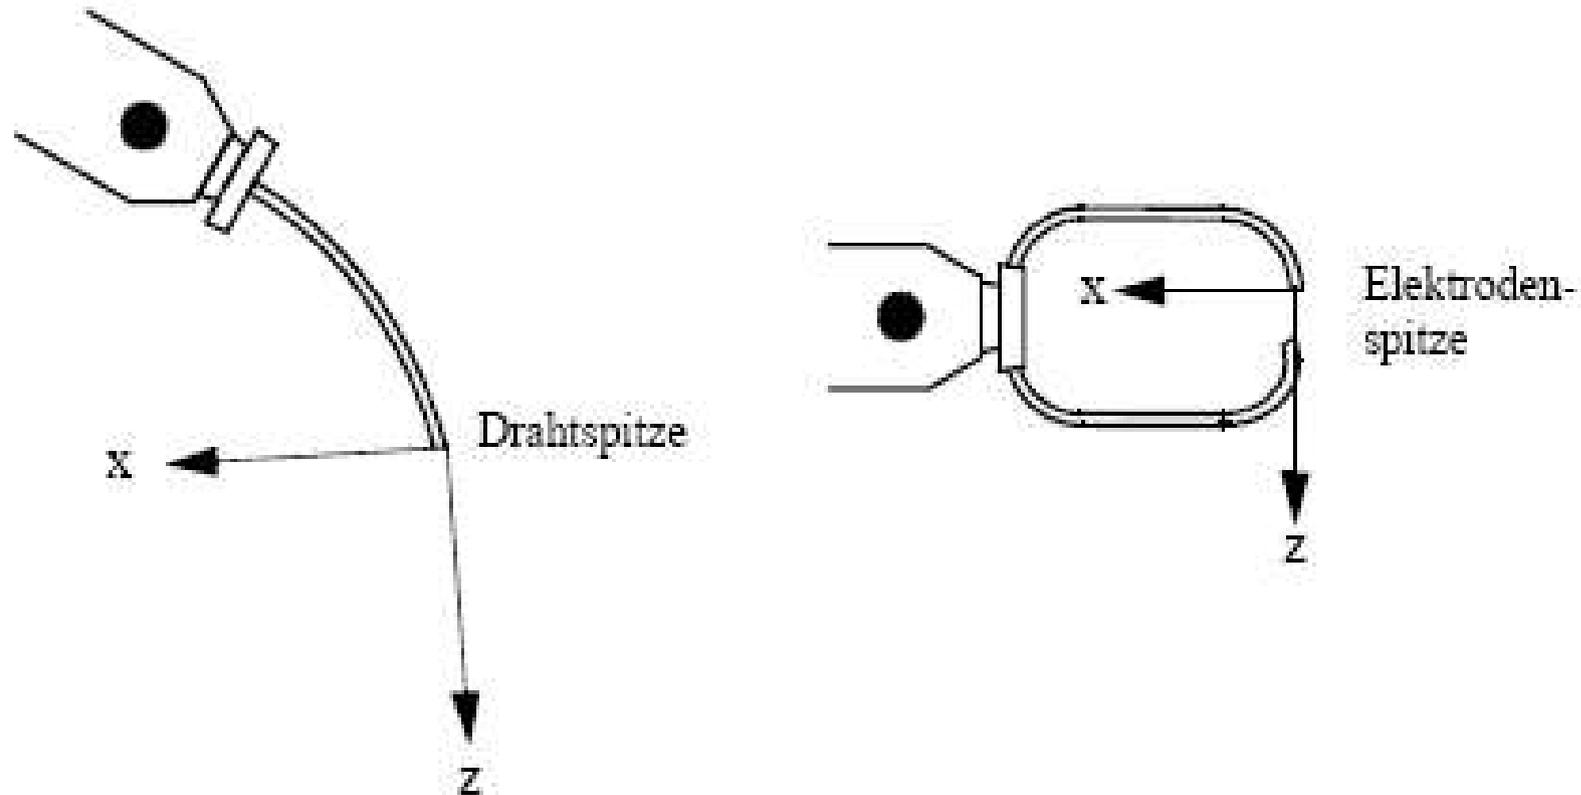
Das Werkzeug-Koordinatensystem, wie es gewöhnlicherweise für einen Lichtbogen-schweißbrenner (links) oder eine Punktschweißzange (rechts) definiert wird.
